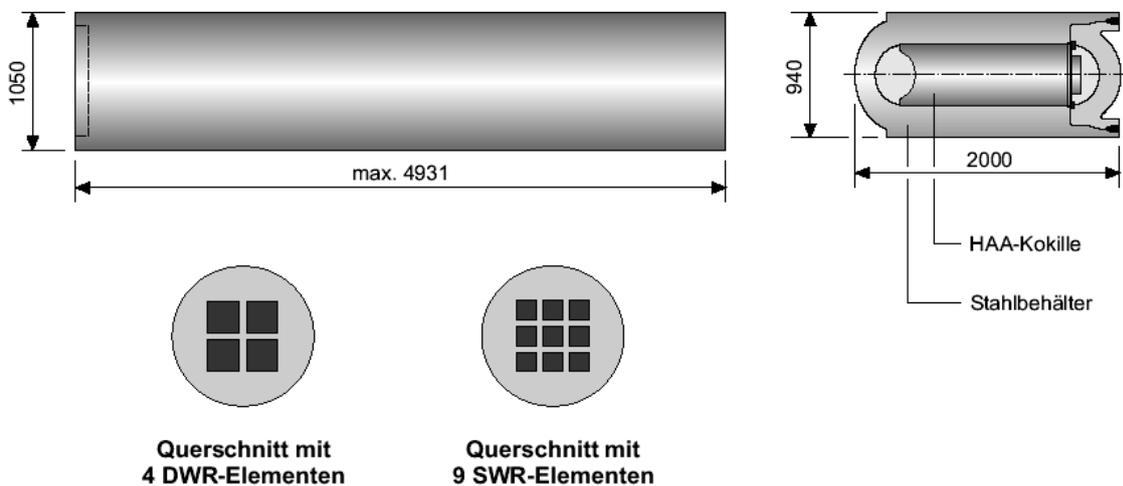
Endlagerbehälter (Stahlbehälter) für ausgediente Brennelemente (links) und HAW-Kokillen (rechts), Abmessungen in mm /3-45/
